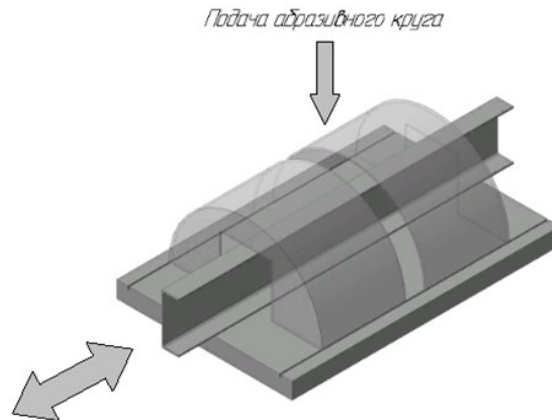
Схема шумозащиты устройства при абразивной обработке сварных швов стержневых конструкций
